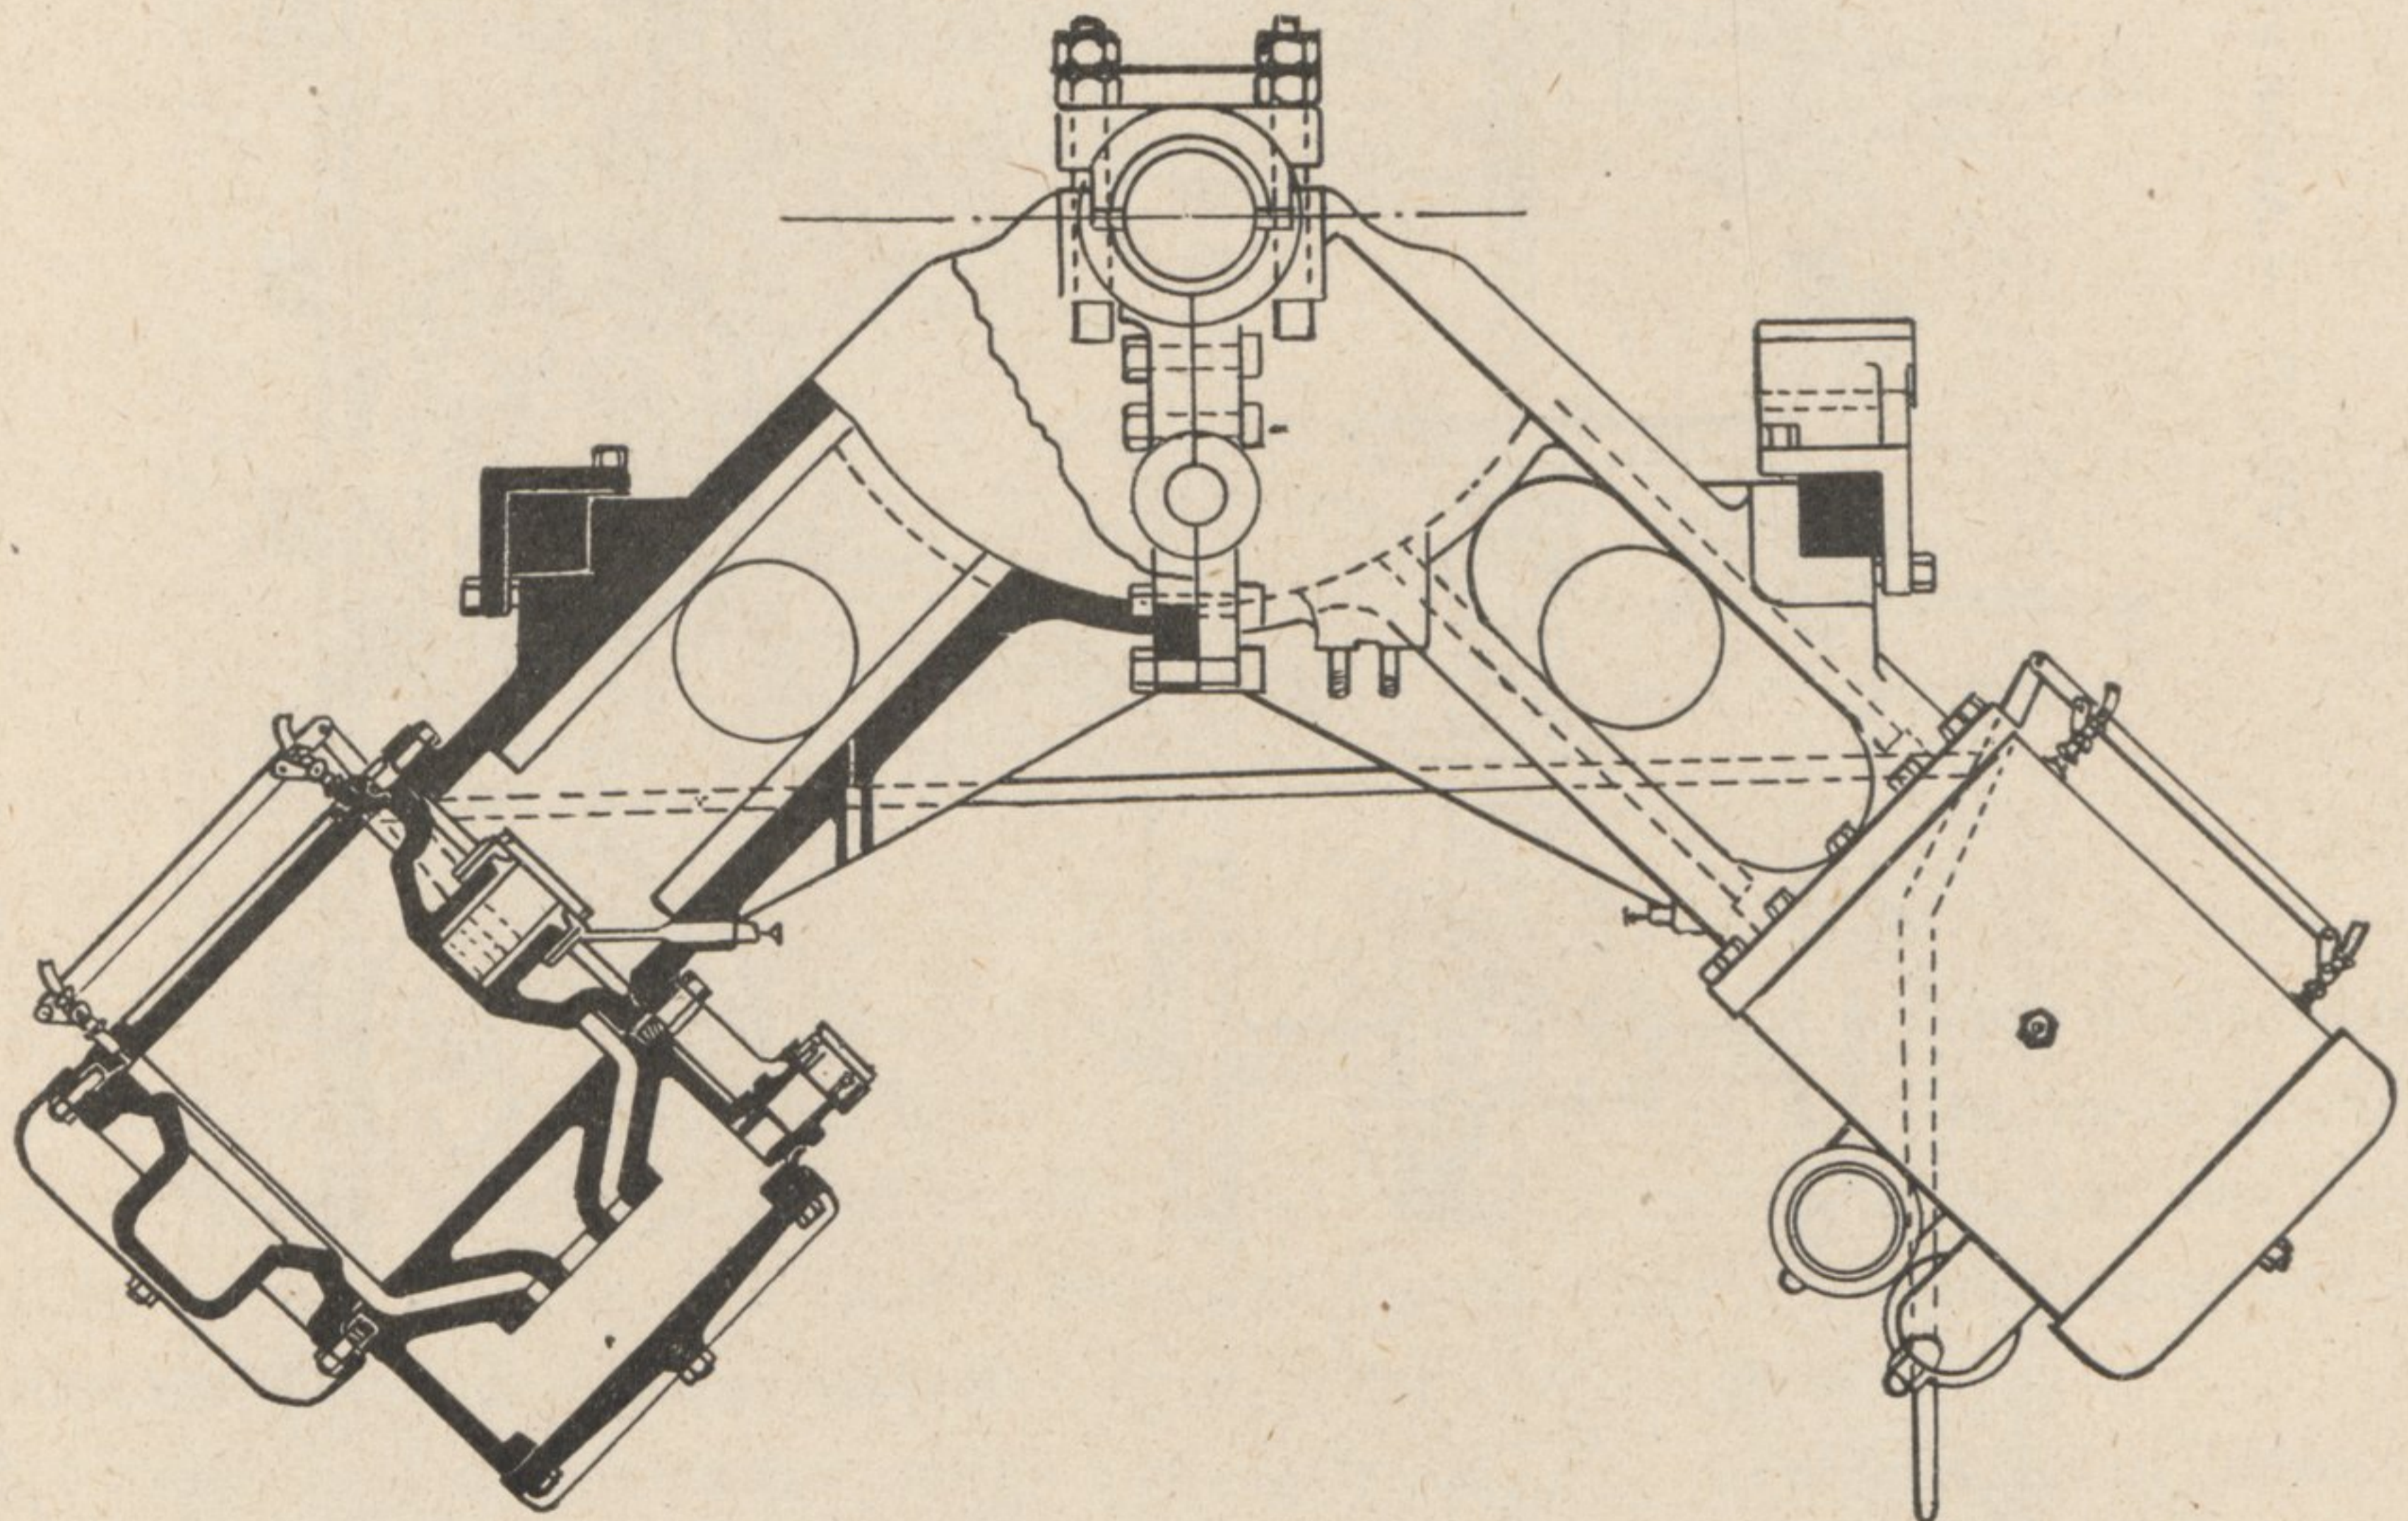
MACHINE (CYLINDRES) DES LOCOMOTIVES A ENGRENAGES, SYSTÈME HEISLER.
